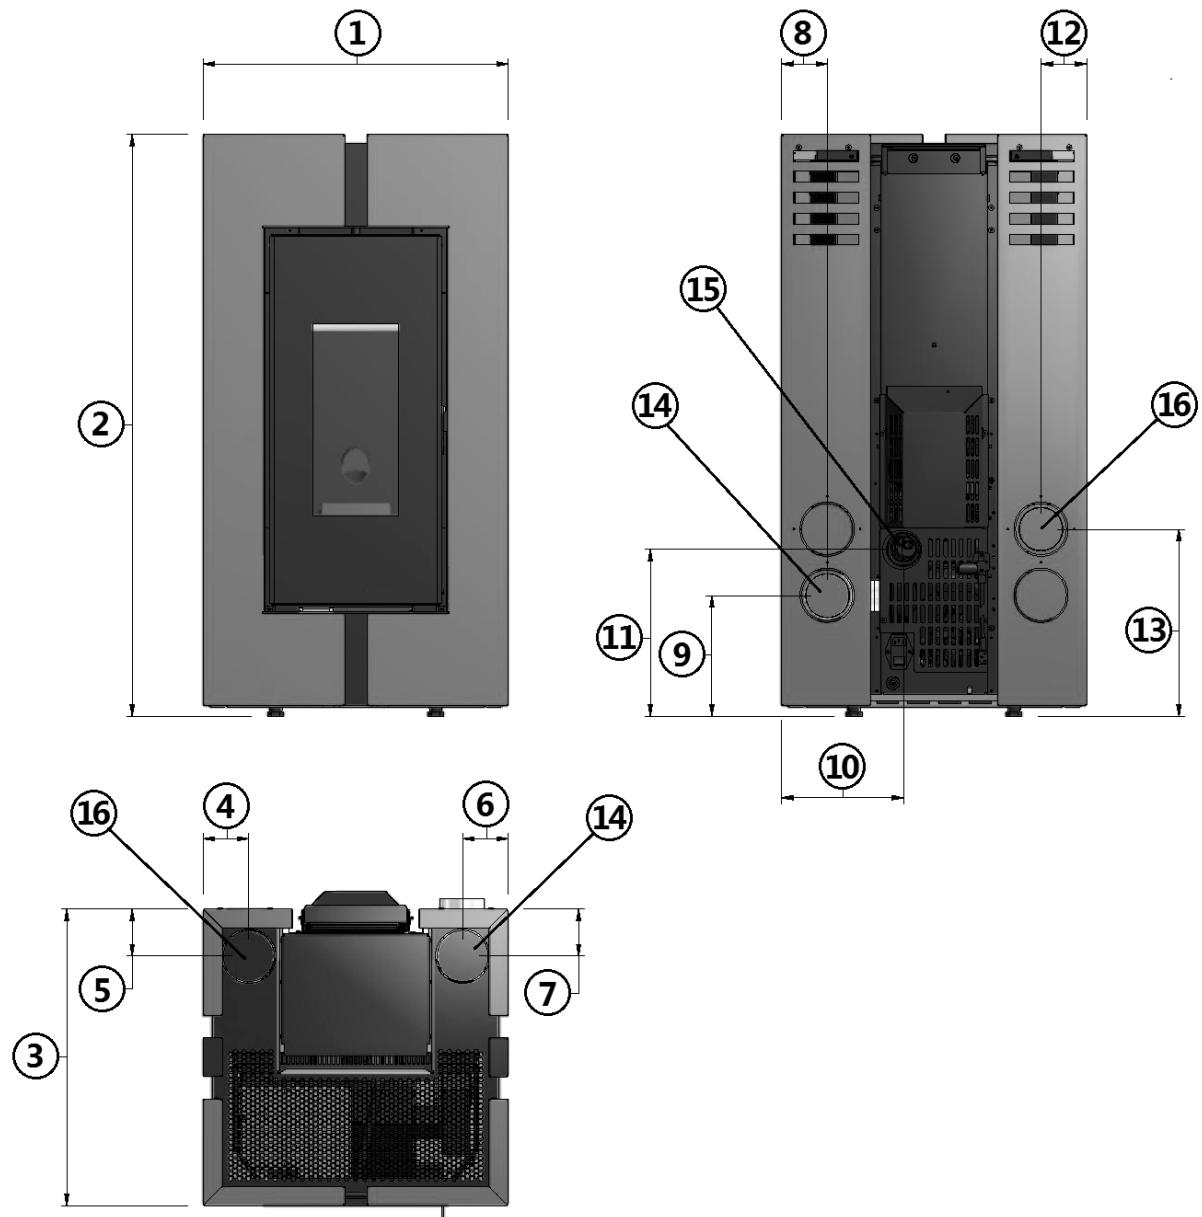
Γενικές διαστάσεις: Doge³ Plus 11KW
